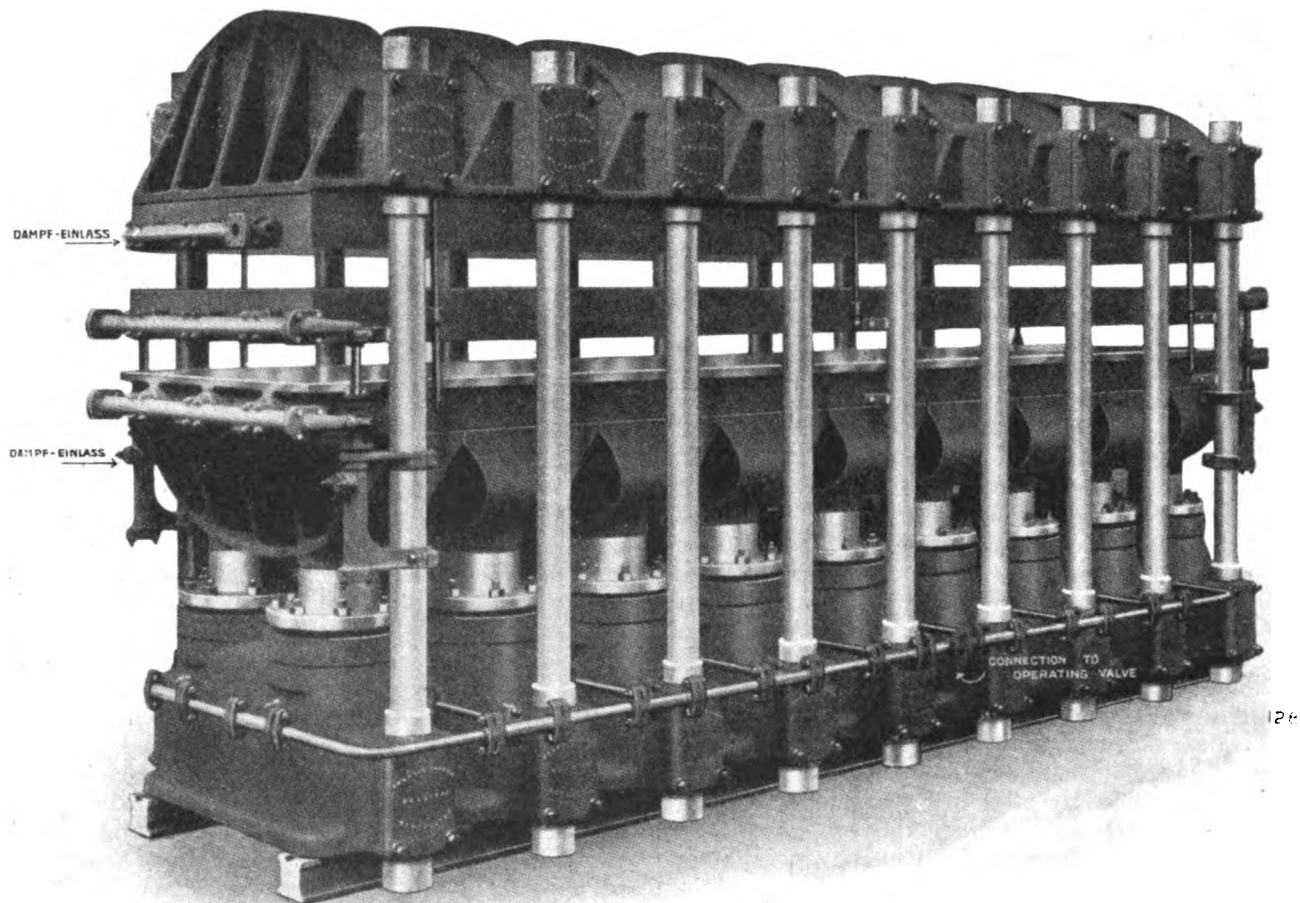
Hydraulische Vulkanisierpresse von Francis Shaw & Co. Ltd. (Bradford-Manchester). Plattengröße 1370 × 6250 mm.
